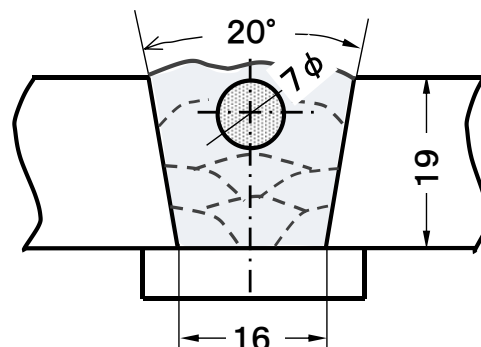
全溶着鋼より溶接試験片を採取する位置
